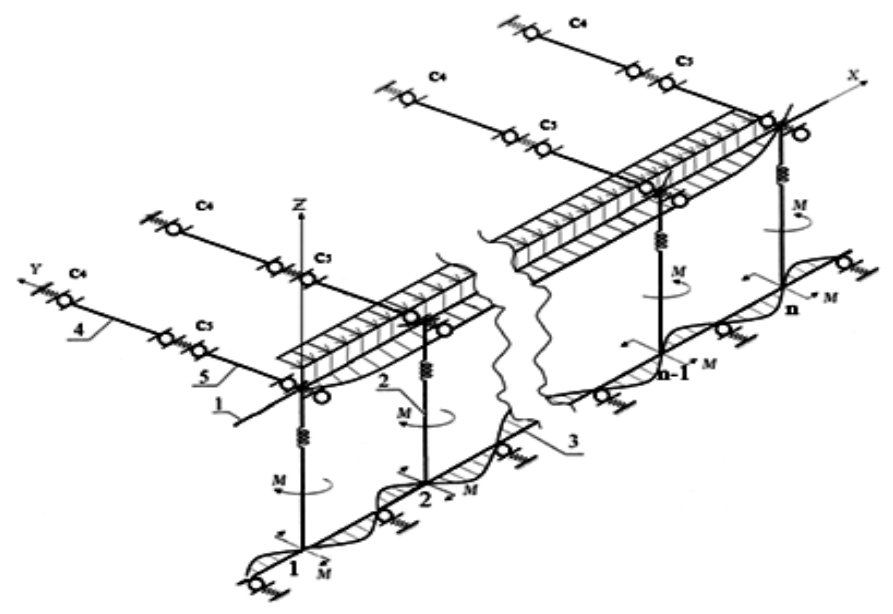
Схема упругих связей батанного механизма станка типа СТР
